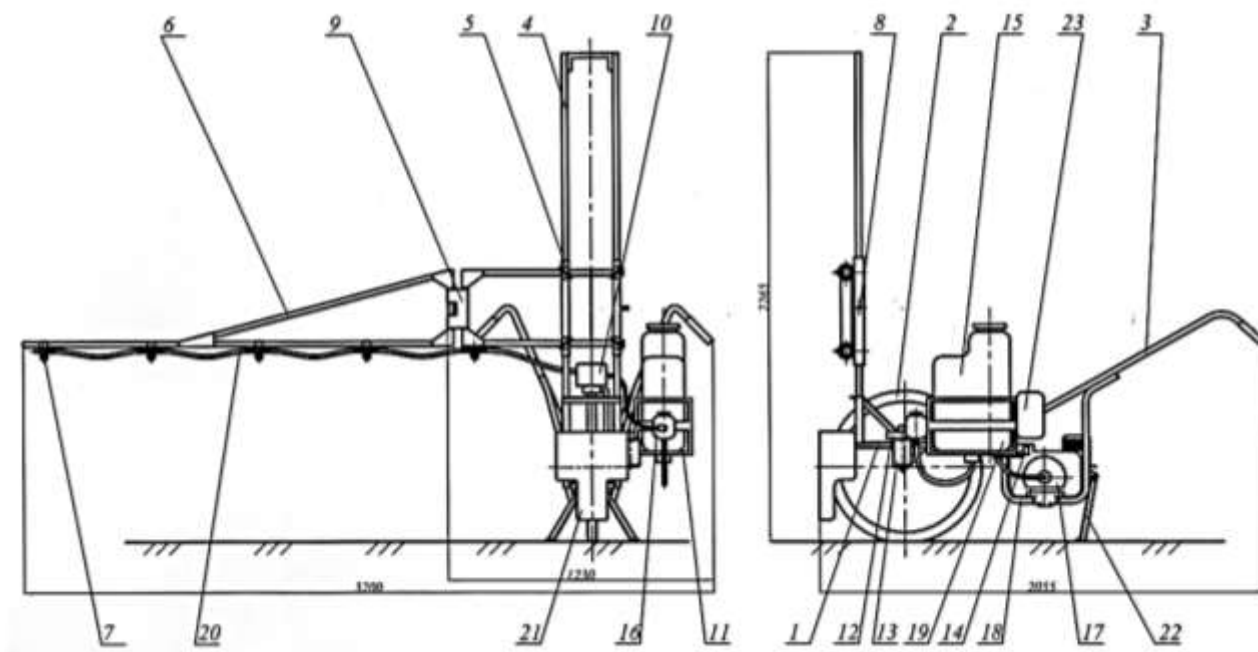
Схема малогабаритного штангового опрыскивателя:
